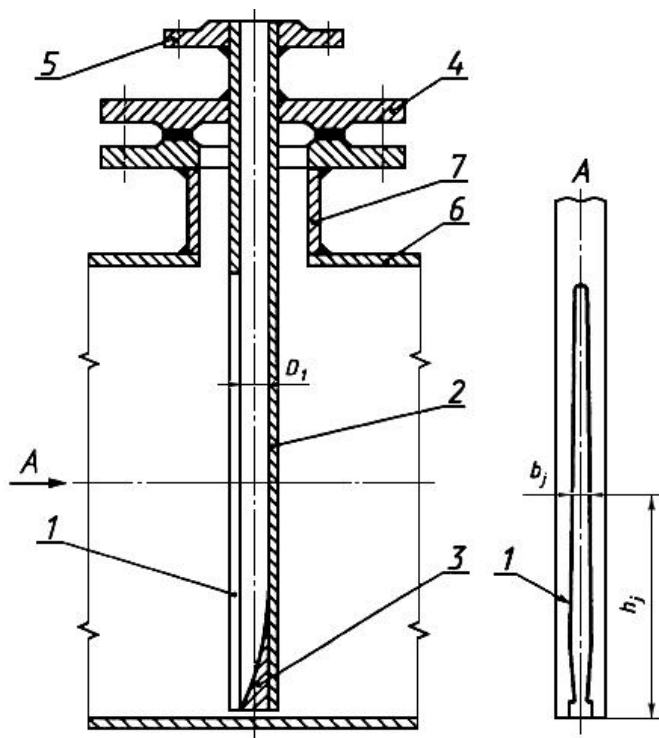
Пробозаборное устройство щелевого типа с одним отверстием: 1 - отверстие; 2 - трубка; 3 - стабилизатор; 4 - крышка; 5 - штуцер; 6 - трубопровод; 7 - монтажный патрубок
